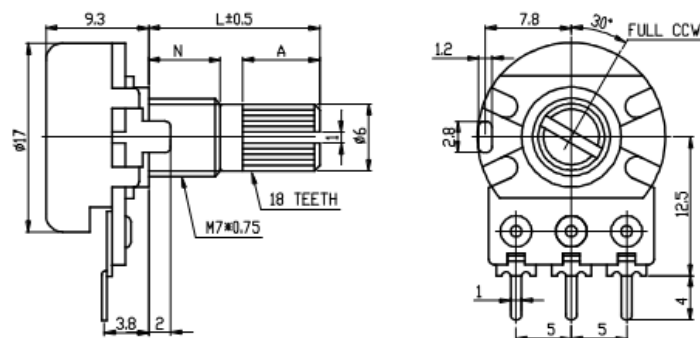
Розміри змінного резистора 16K1-A100K
